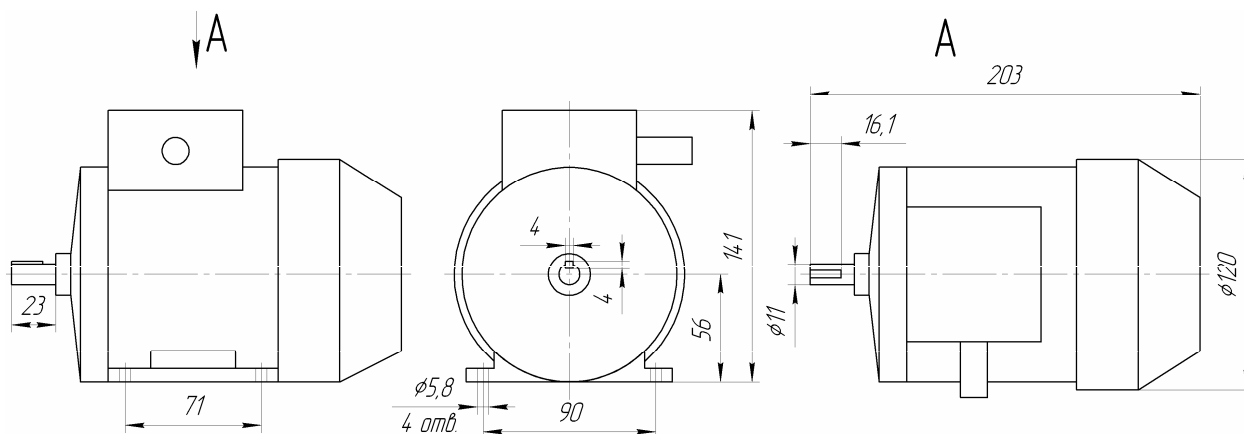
Эскиз и главные размеры асинхронных двигателей серии 4А
